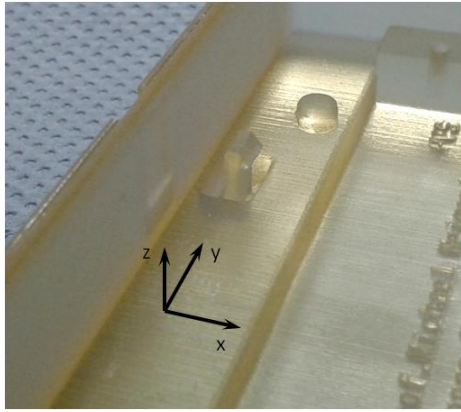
Detailansicht eines Schnapphakens zur Platinenfixierung
